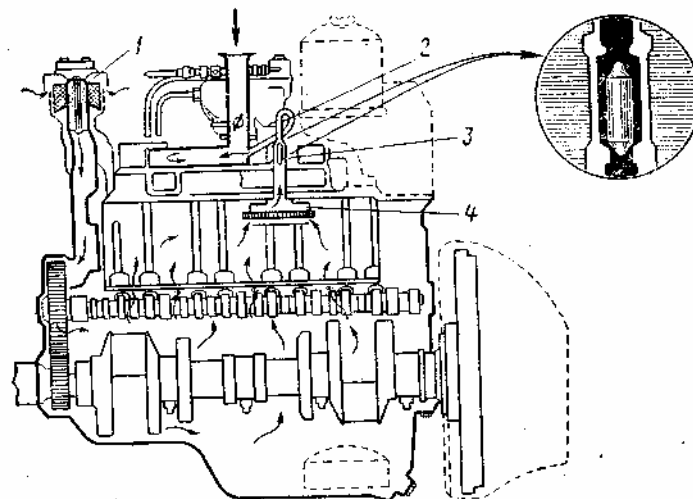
Схема вентиляции картера двигателя ЗИЛ-130
